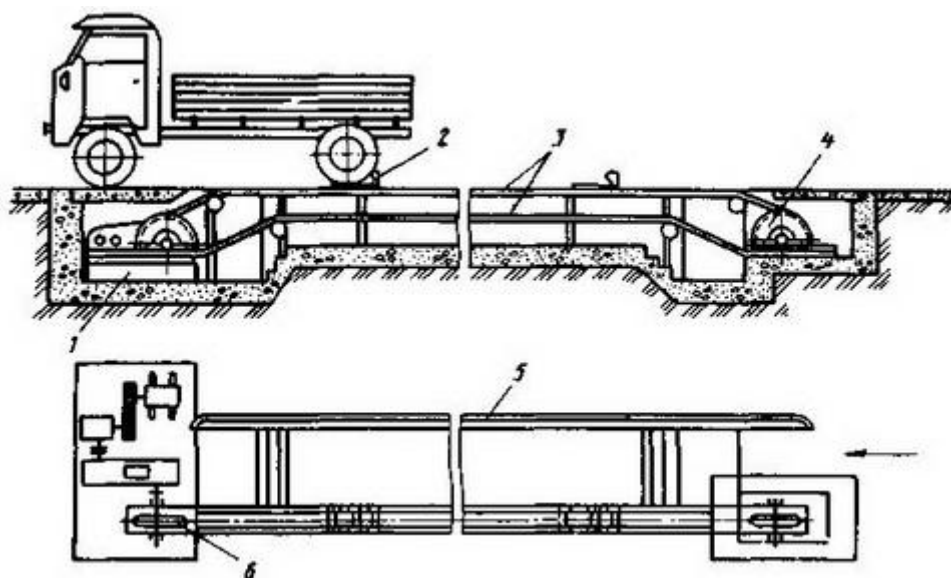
Принципиальная схема толкающего конвейера: 1 — приводная станция; 2 — толкающая тележка; 3 — цепи; 4 — натяжная станция; 5 — направляющая пути; 6 — ведущая звездочка
